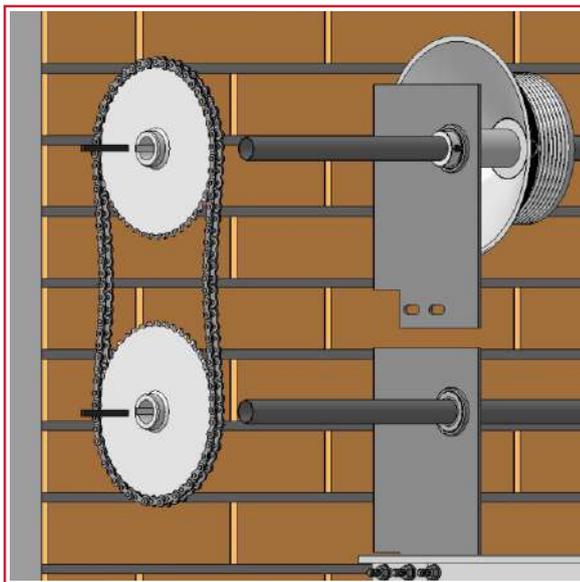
Установка цепного привода на двухвальной системе с расположением устройства натяжения цепи снаружи
